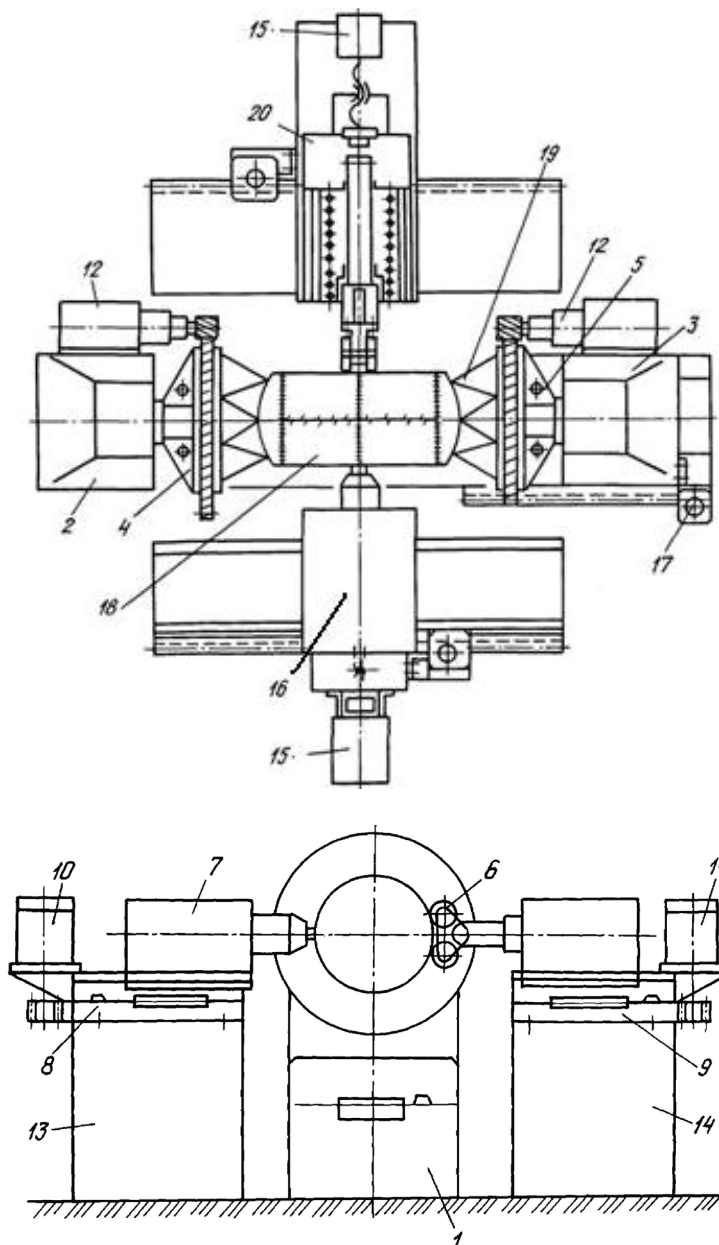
Схема сварочной установки СБ-2000:
